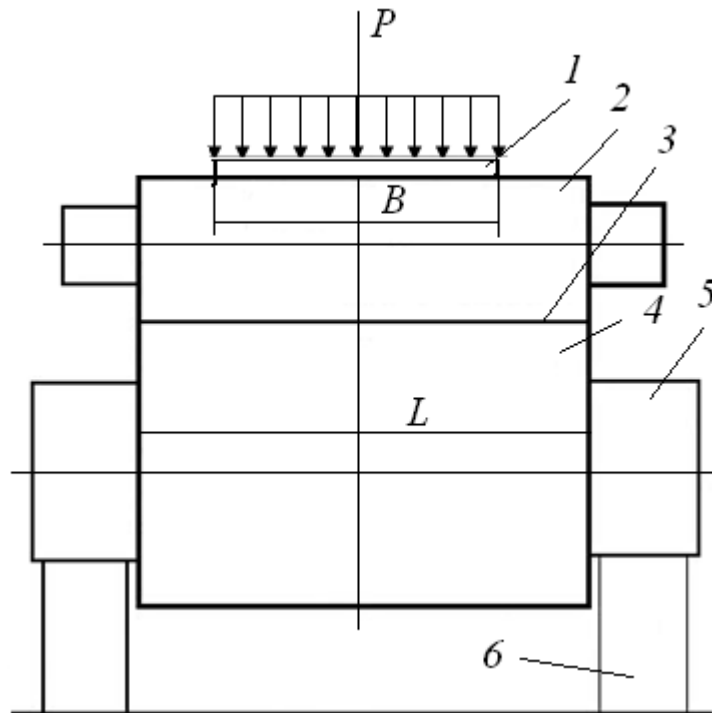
Схема установки для дослідження між валкового тиску: 1 - смуга; 2 - робочий валок; 3 - копіювальний папір; 4 - опорний валок; 5 - шийка опорного валка; 6 - опора; 7-опорна плита.
